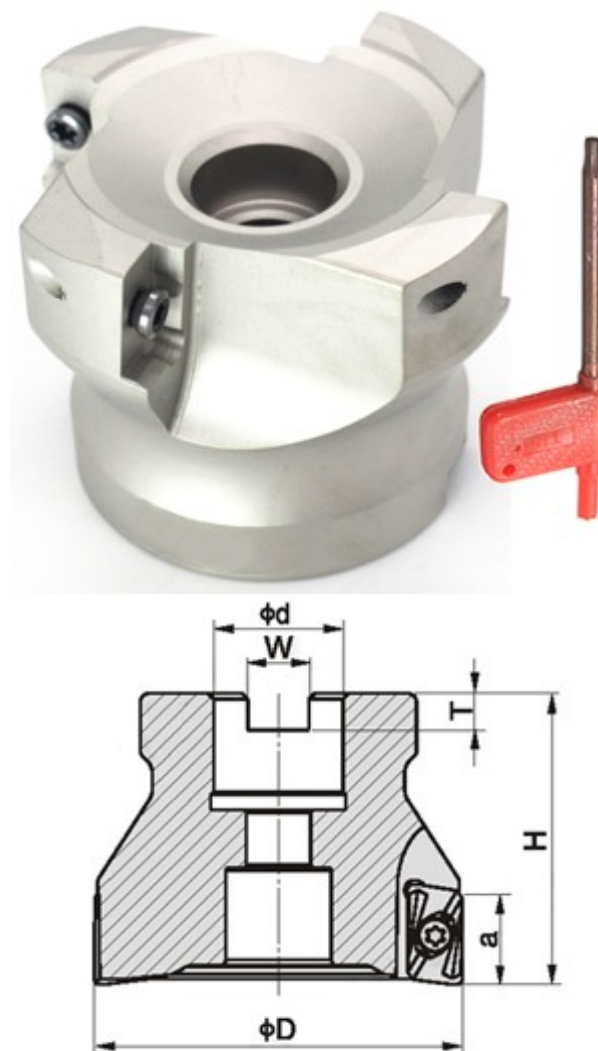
5. Насадна торцева фреза ВАР 400R
